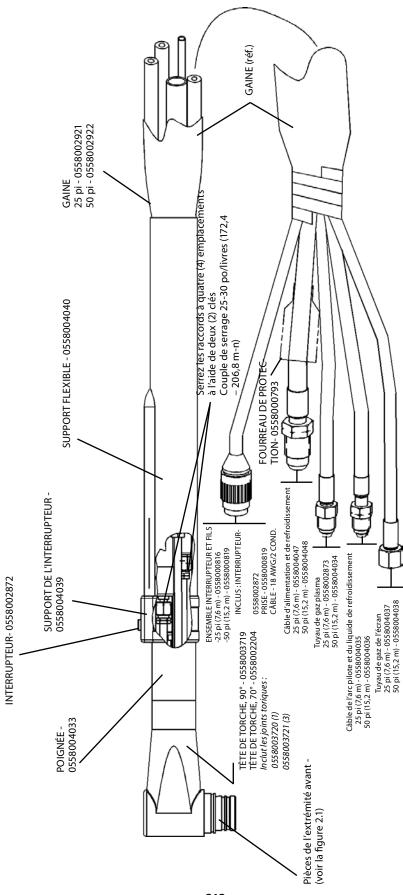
Pièces de rechange - ensemble de la torche PT-26
